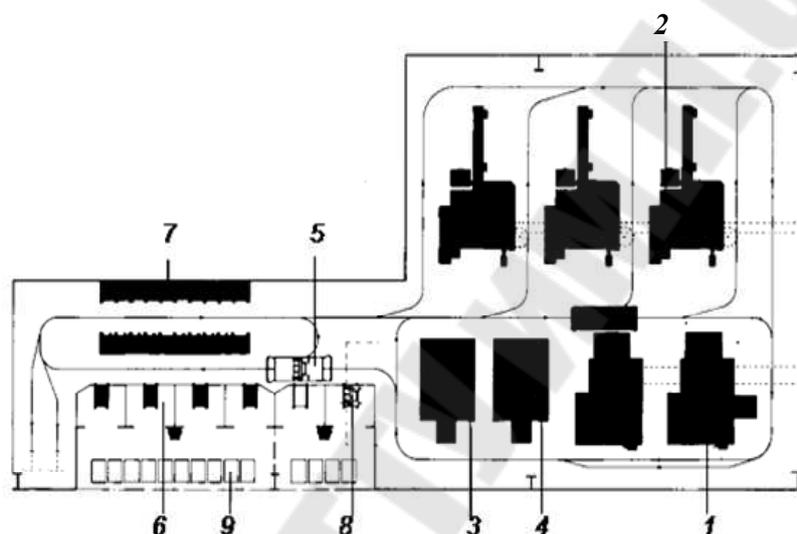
Компоновка оборудования ГПО, состоящего из обрабатывающих центров и транспортного оборудования: 1 – обрабатывающие центры; 2 – вертикально-токарные станки; 3 – хонинговальный станок; 4 – измерительная координатная машина; 5 – индуктивная тележка для транспортировки деталей и инструментов; 6 – места установка деталей; 7 – накопители палет для изделий; 8 – место подготовки инструмента; 9 – склад хранения заготовок и готовых деталей
